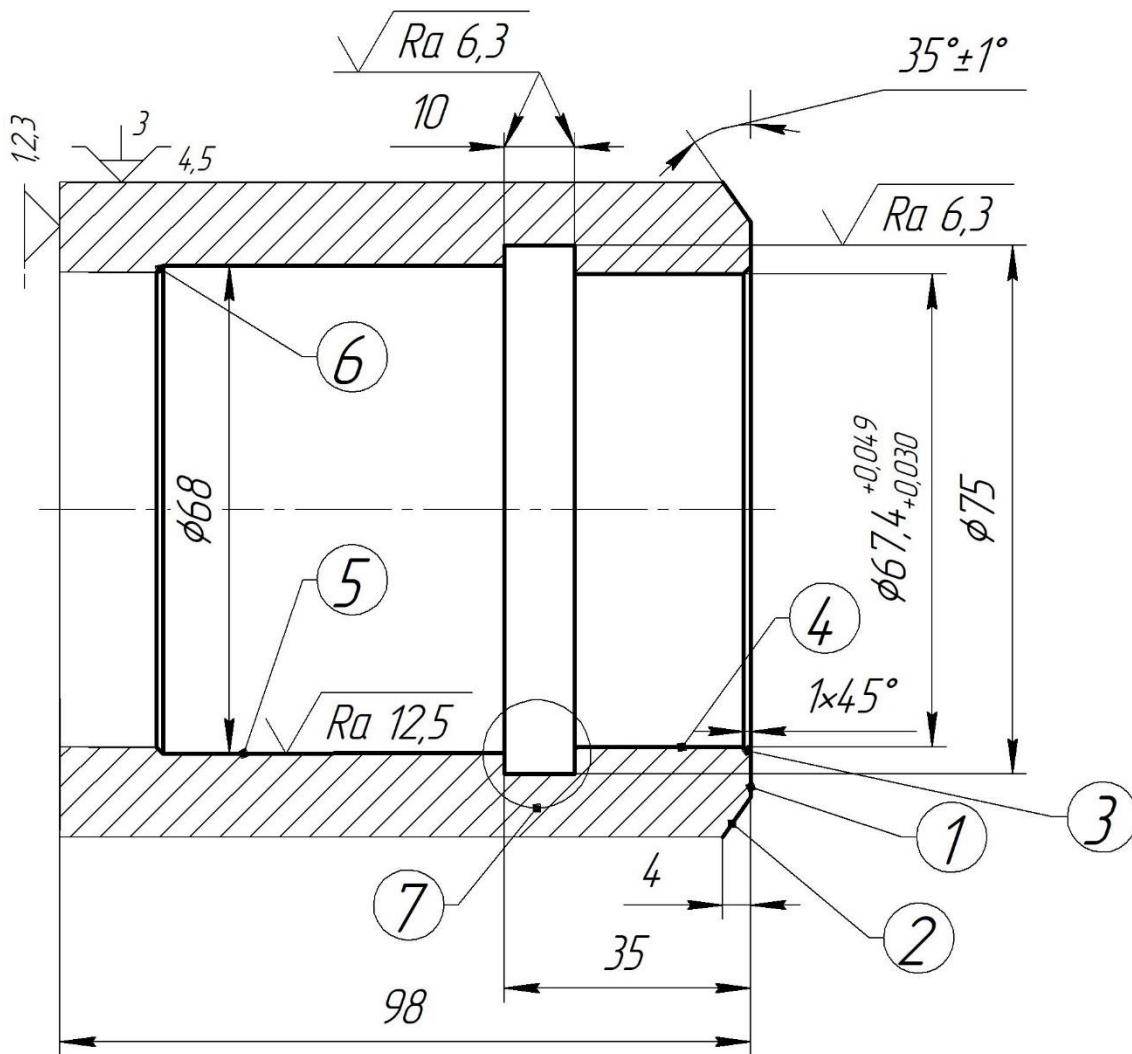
Схема установки заготовки на операції 025 установ А
